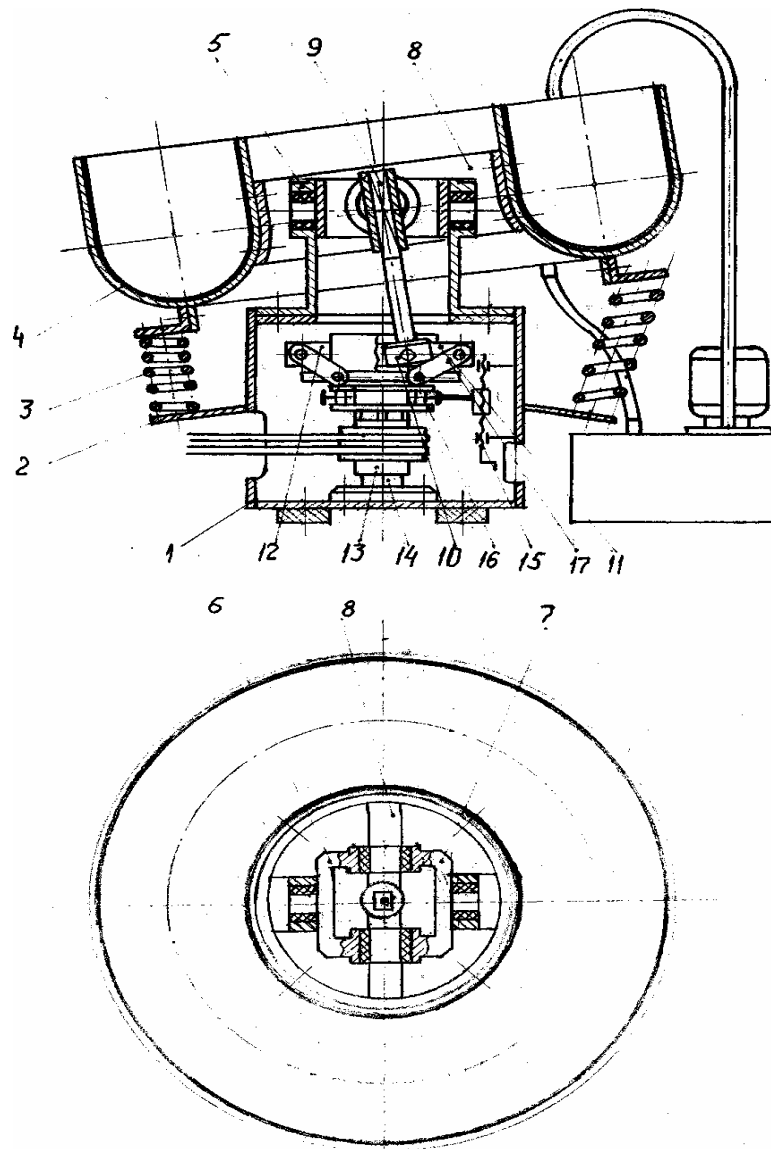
Конструктивна схема вібраційно-відцентрової установки
